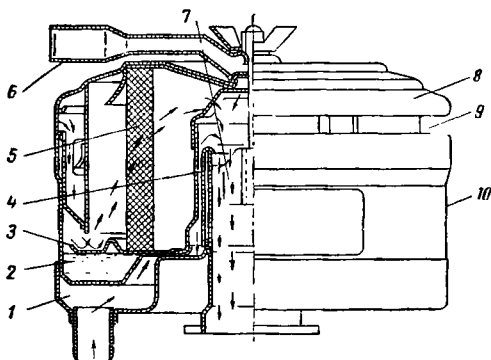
Воздушный фильтр карбюратора двигателя ГАЗ-51.
